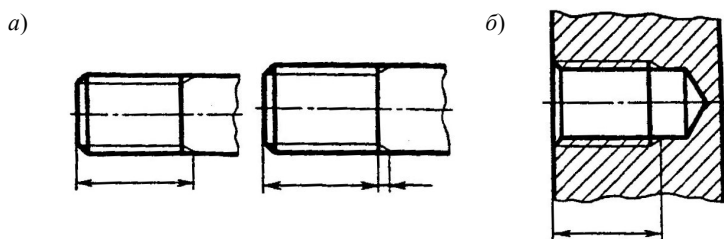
Обозначение размера длины резьбы со сбегом:
